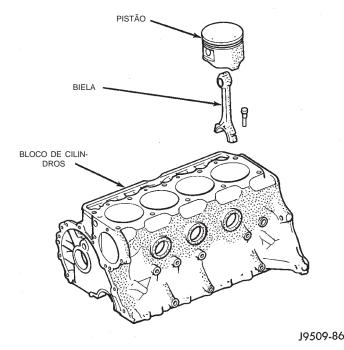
Remoção do Conjunto da Biela e do Pistão
